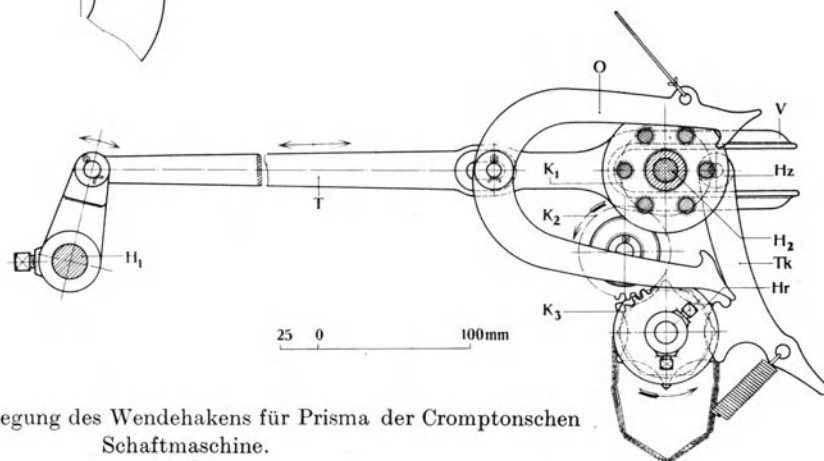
Die Bewegung des Wendehakens für Prisma der Cromptonschen Schaftmaschine.
